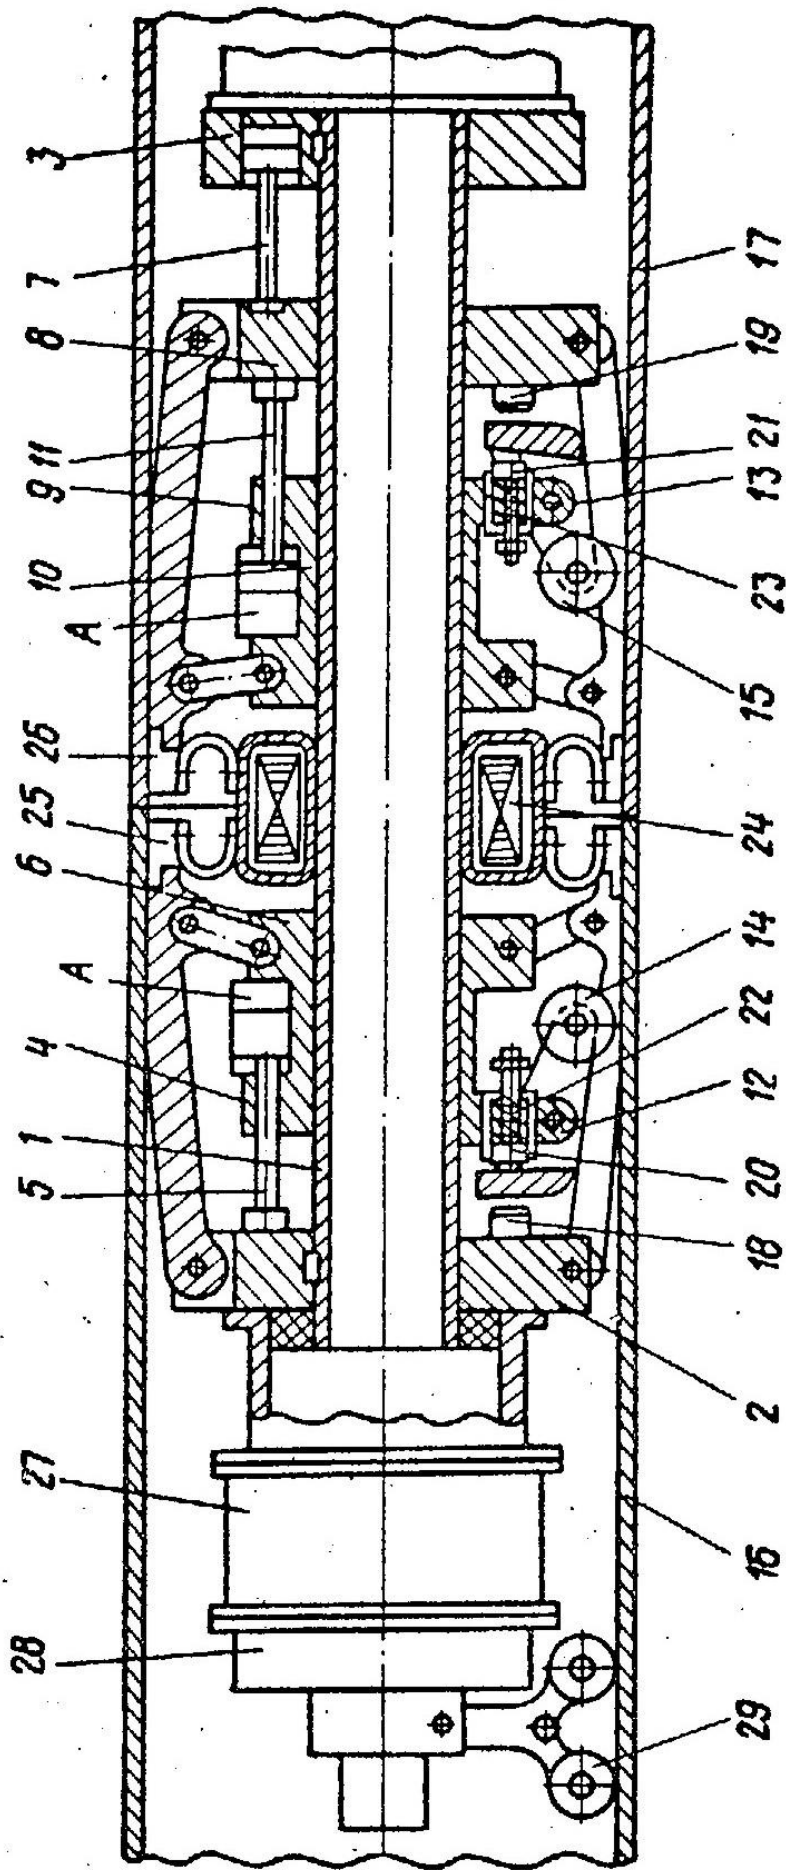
Машина для контактной стыковой сварки трубопроводов
